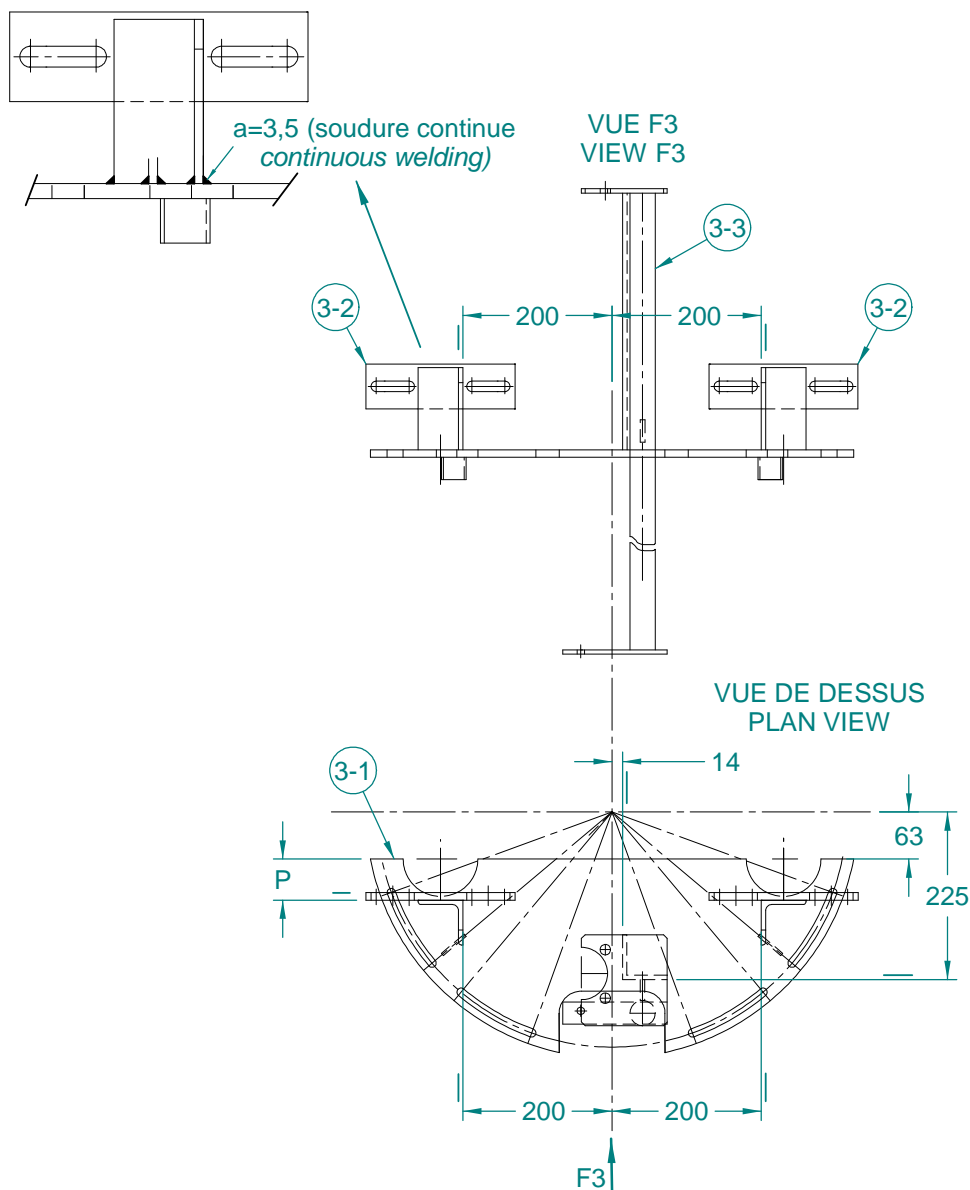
DETAILS PIECE REP.3 (PLAQUE D'ASSECHEMENT ET CONROLEUR (SUITE))
